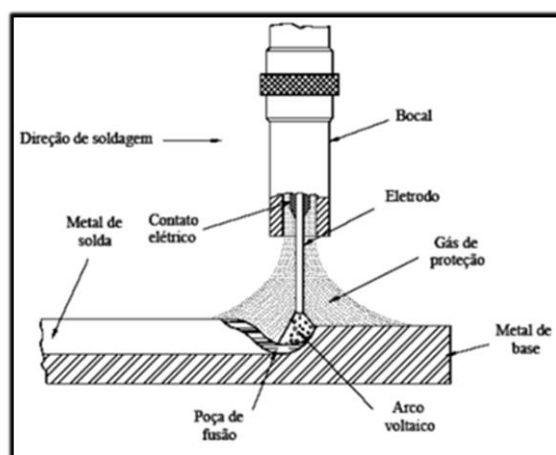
Detalhe do processo de soldadura GMAW [39].
